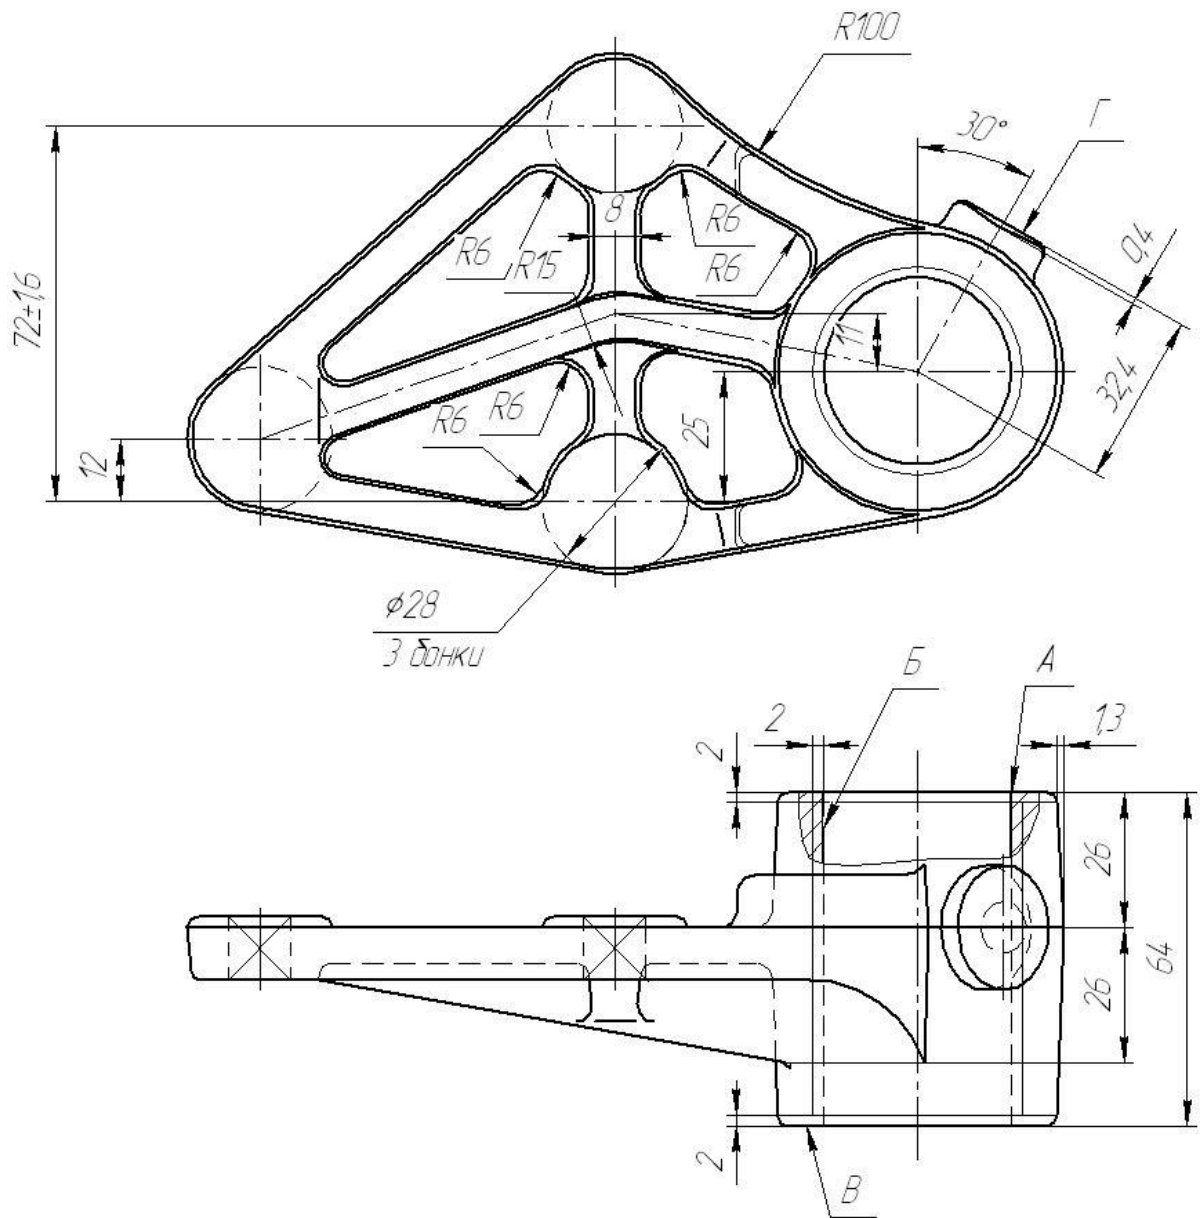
Підшипник з нанесеними припусками на механічну обробку
